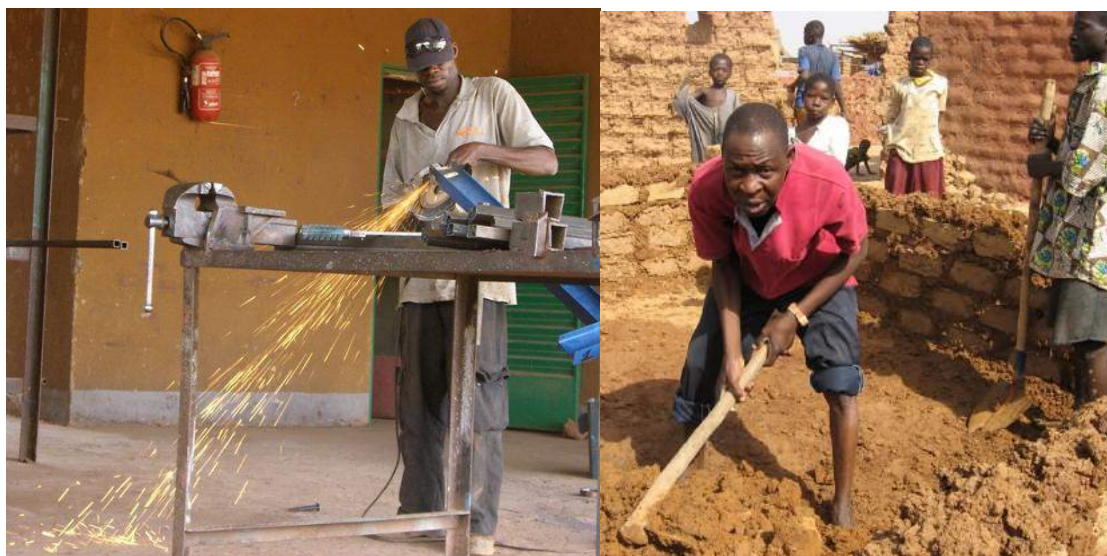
& 12: Adama (Metallbearbeitung) und Sayouba (Hausbau) immer mit Engagement bei der Sache
